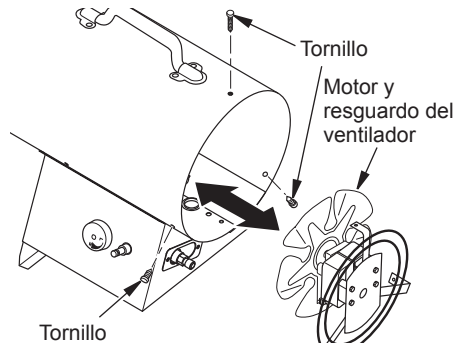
Desmontaje/reemplazar del motor y el resguardo del ventilador del calentador
